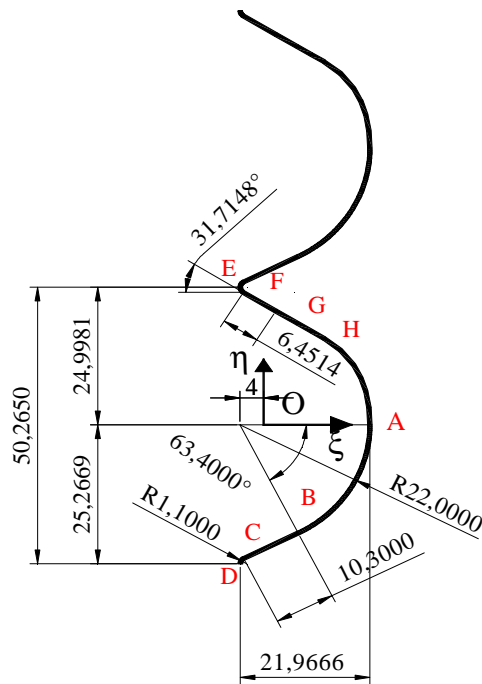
Forma constructivă a profilului transversal al cremalierii generatoare, varianta I
